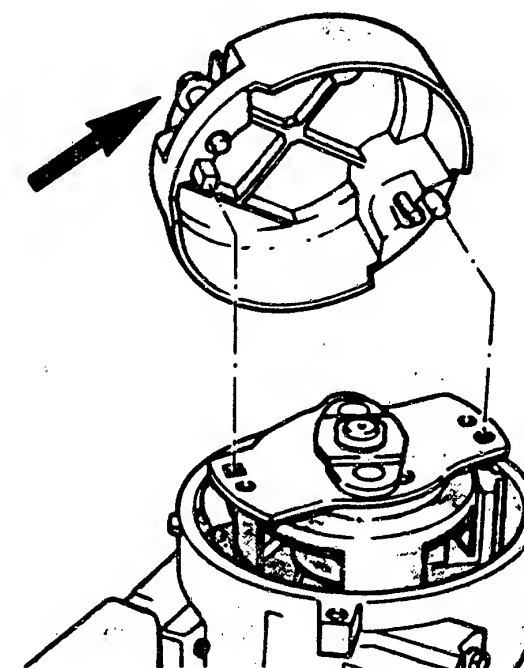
Aufnahme des Rotors am Zündverteiler des 2,0l-Einspritzmotors. Die Rotorpole (Pfeil) müssen mit Silikon-Fett beschichtet sein.
